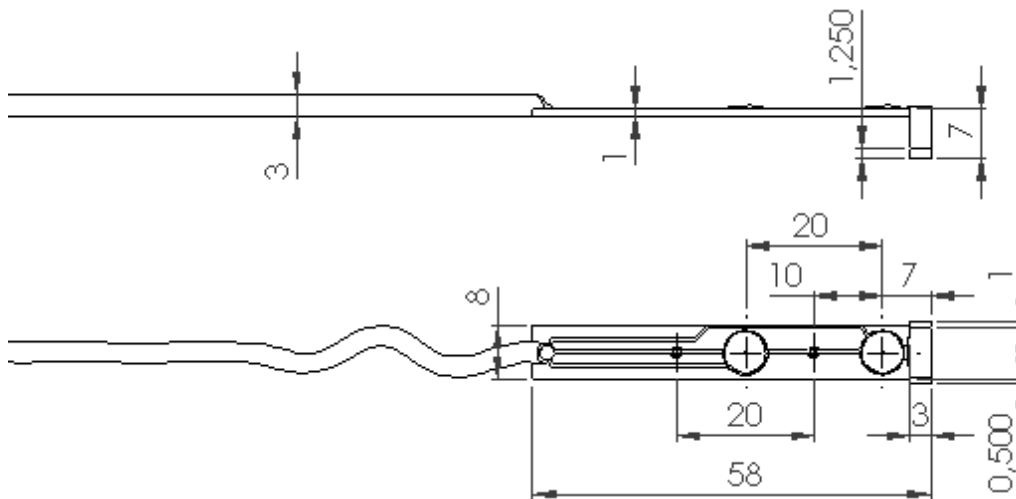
Dimensions de la placa de circuit imprès amb cables i contactors soldats.
